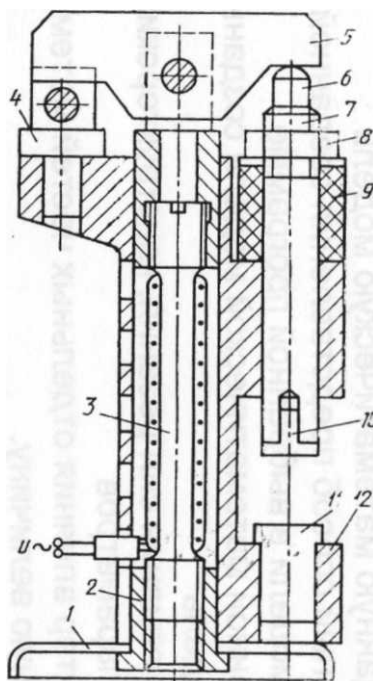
Пресс для штамповки с узлами из материала с ТМП
